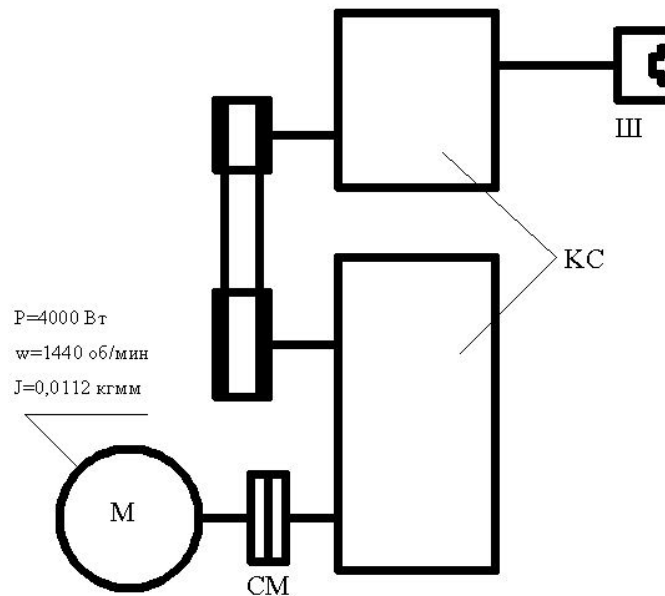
кінематична схема механізму поздовжньої подачі стола верстата .
